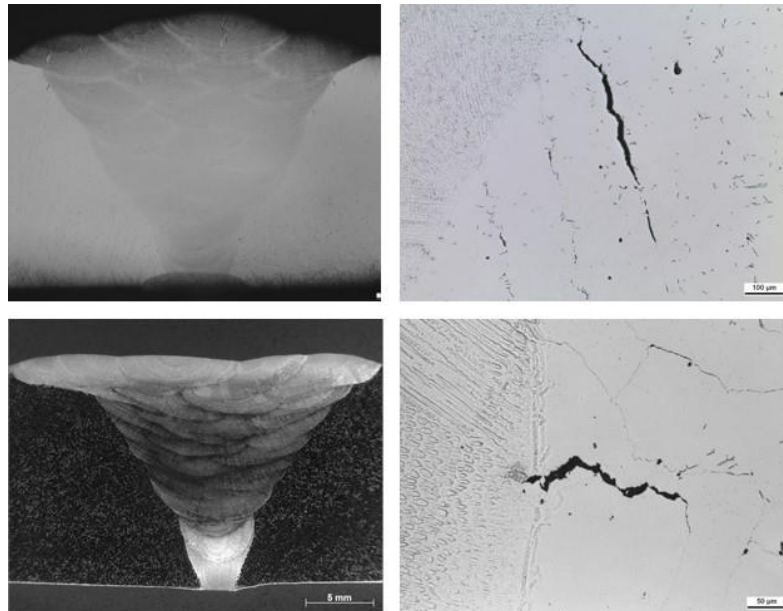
Makro- und Mikroaufnahmen der heißrissbehafteten Nahtquerschliffe der Schweißnähte am Schleuderguss aus Alloy 625 (oben: E-Hand, unten: mWIG) [12].
